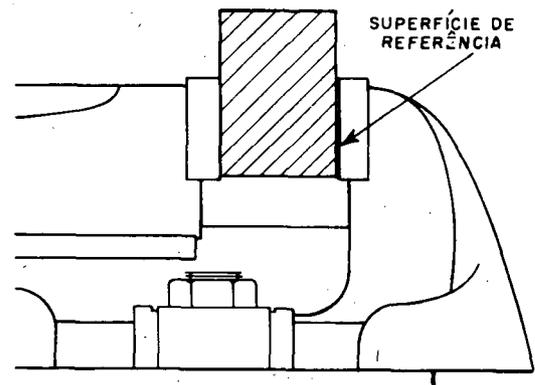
Superfície de referência do material (SR) apoiada na mandíbula móvel para se obter, com a fresagem, uma superfície perpendicular.
